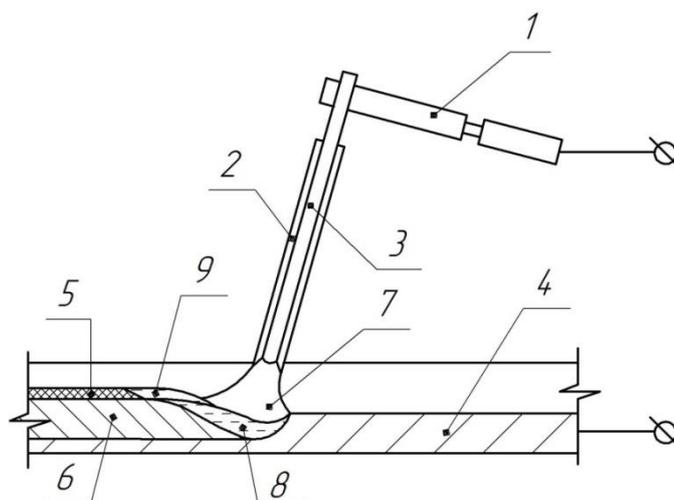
Схема осуществления сварки самозащитной порошковой проволокой
